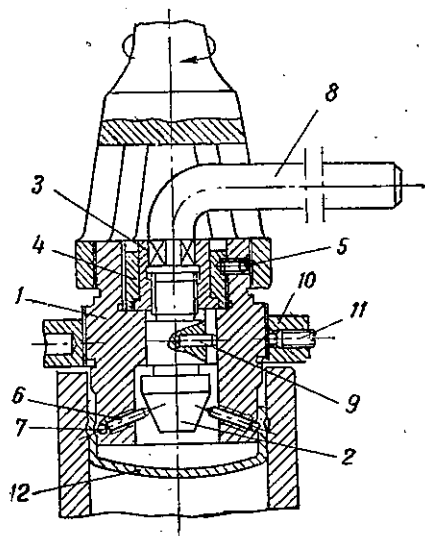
Mandrină cu bile pentru flanșe oarbe
